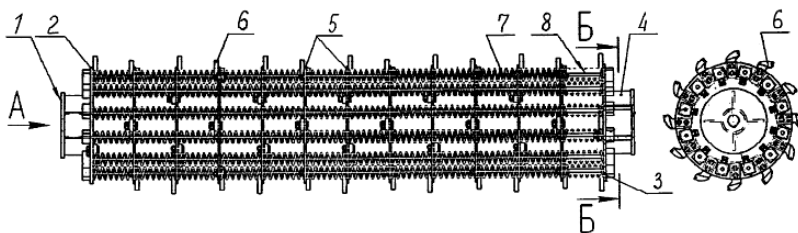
Конструктивная схема рабочего органа скальвателя льда:
